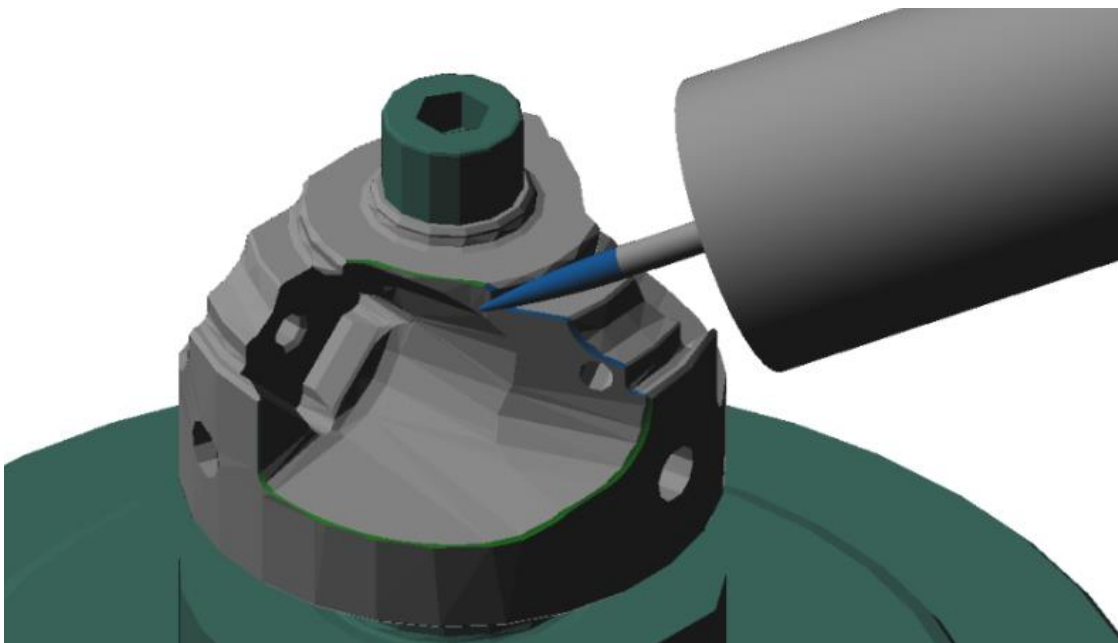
Skica technické frézy pro reprezentaci nástroje
